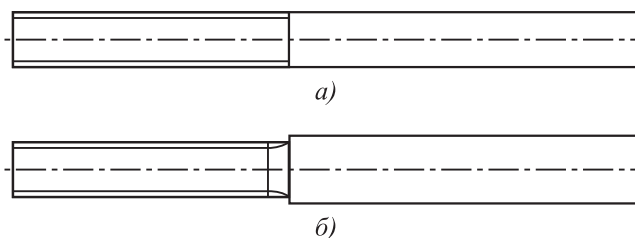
Изделия с резьбой, расположенной на части его длины:
